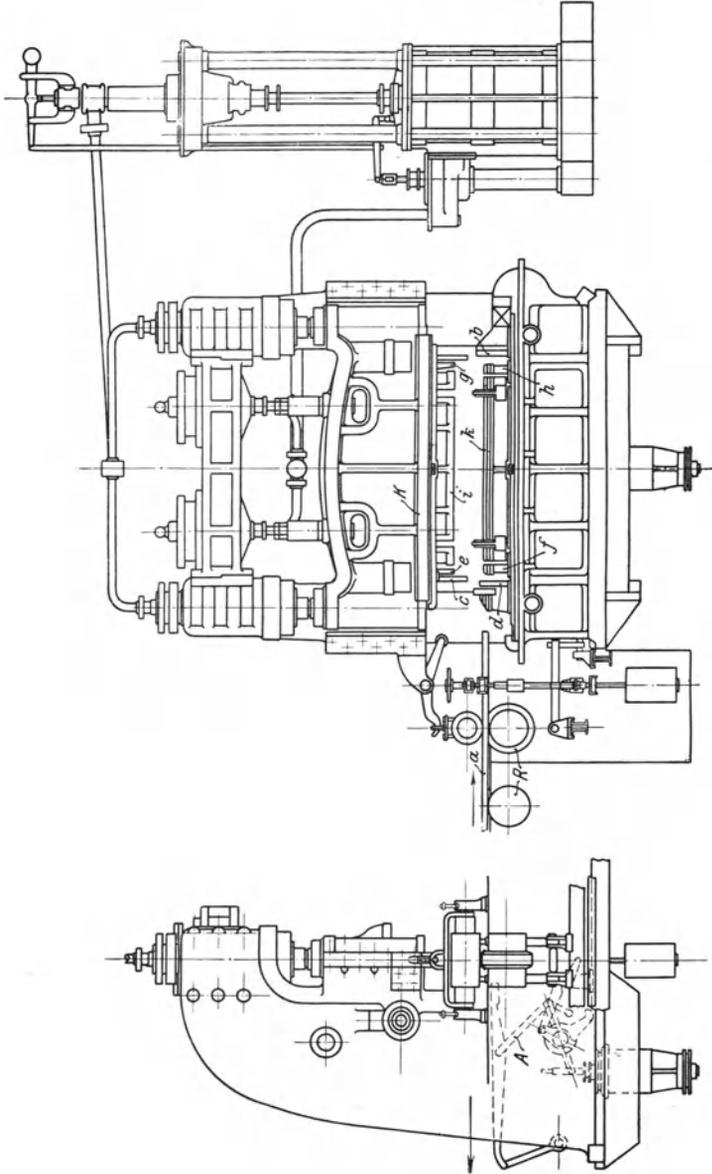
Schwellen-Schneid-, Kapp- und Richtmaschine.
